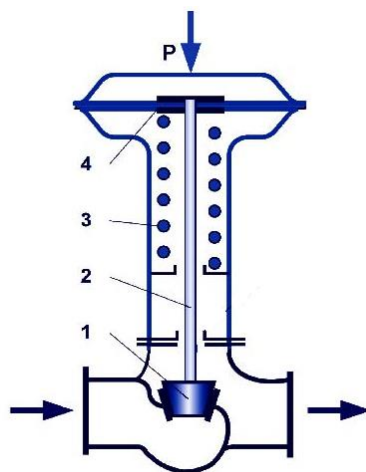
Схема мембранного исполнительного механизма, установленного на регулирующем клапане: 1 - регулирующий орган; 2 - шток; 3 - пружина; 4 - мембрана;
